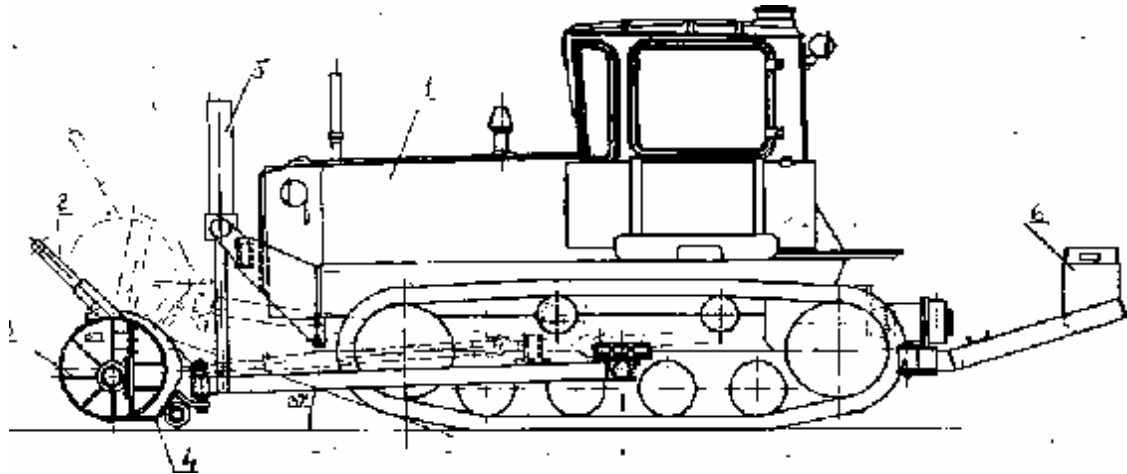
Схема роторного измельчителя кустарника ИК-1,8:
